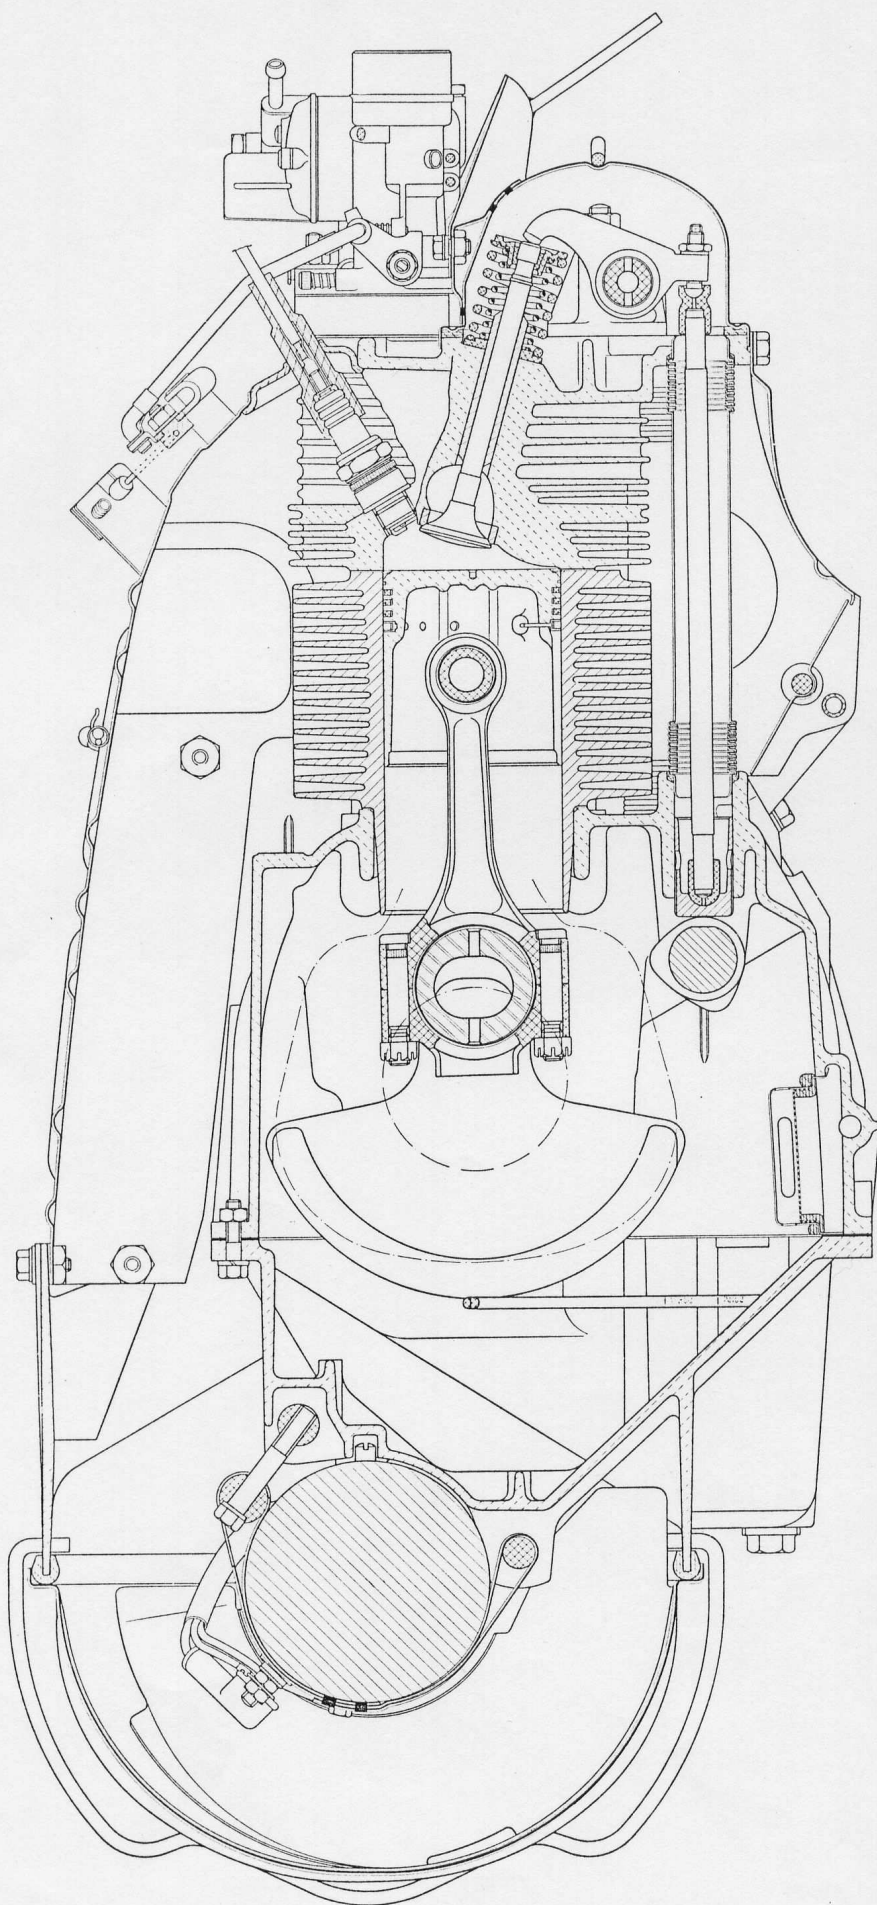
Querschnitt des Motors durch einen Zylinder.
